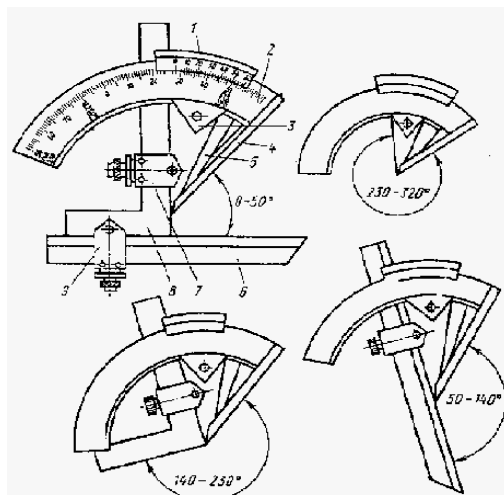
Угломер УН: 1 – нониус; 2 – основание; 3 – стопор; 4 – линейка; 5 – сектор; 6 – съемная линейка; 7 – державка; 8 – Г-образный угольник; 9 – державка
